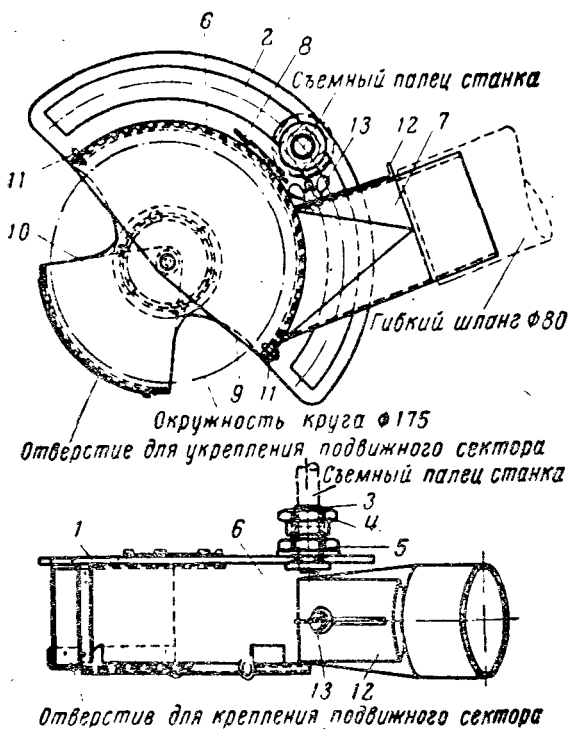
Защитно-обеспыливающий кожух для универсально-шлифовального станка
